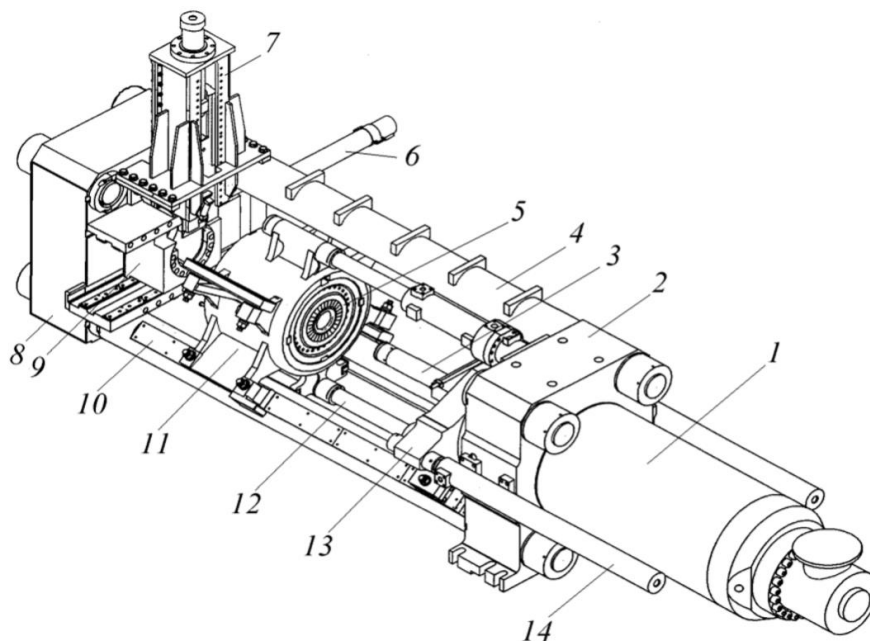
Схема горизонтального гидравлического пресса прямого действия для прессования профилей из алюминиевых сплавов
